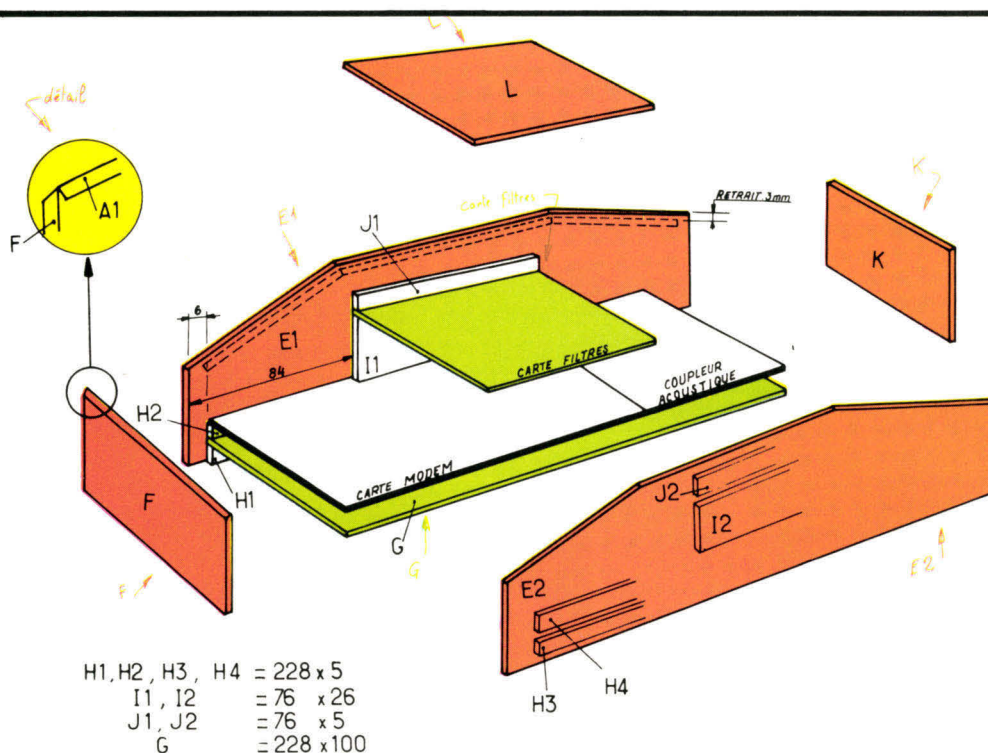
Fig. A. - Vue éclatée du boîtier. Remarquez la disposition des cartes électroniques disposées dans leurs glissières.
